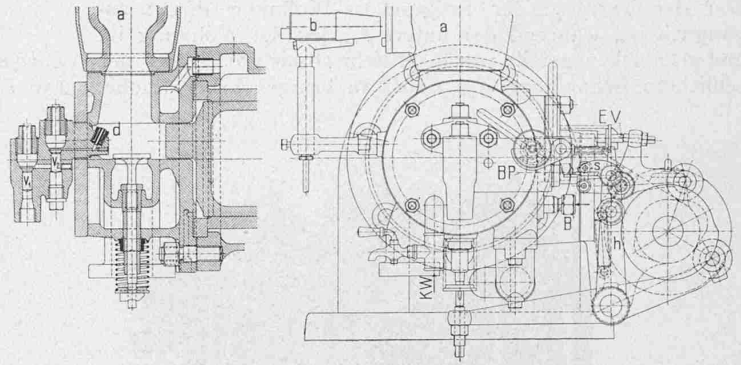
Vert. Längenschnitt und Rückansicht des 5 PS-Glühkopfmotors. — 1 : 10.
